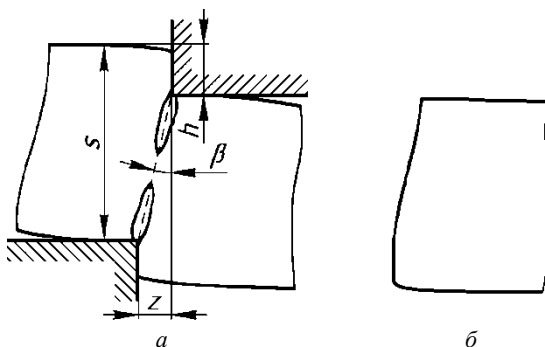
Образование трещин скола (*а*) и форма боковой поверхности отделенной заготовки (*б*)
